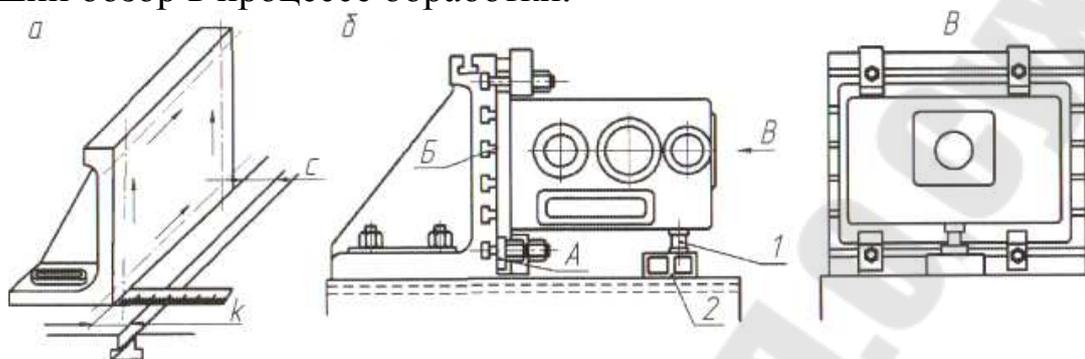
Схема выверки угольника (а) и установка корпуса на угольнике (б): 1 – опоры; 2 – плоская подкладка или брусок; А – крепление заготовки к угольнику; Б – Т-образные пазы угольника
